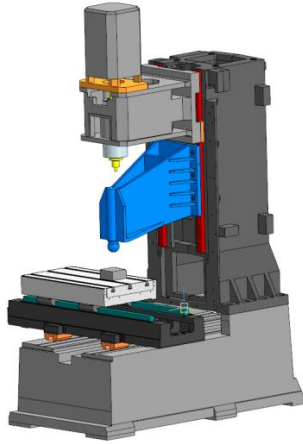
Схема вертикального фрезерного станка с установленной моделью шпиндельной бабки [5].
